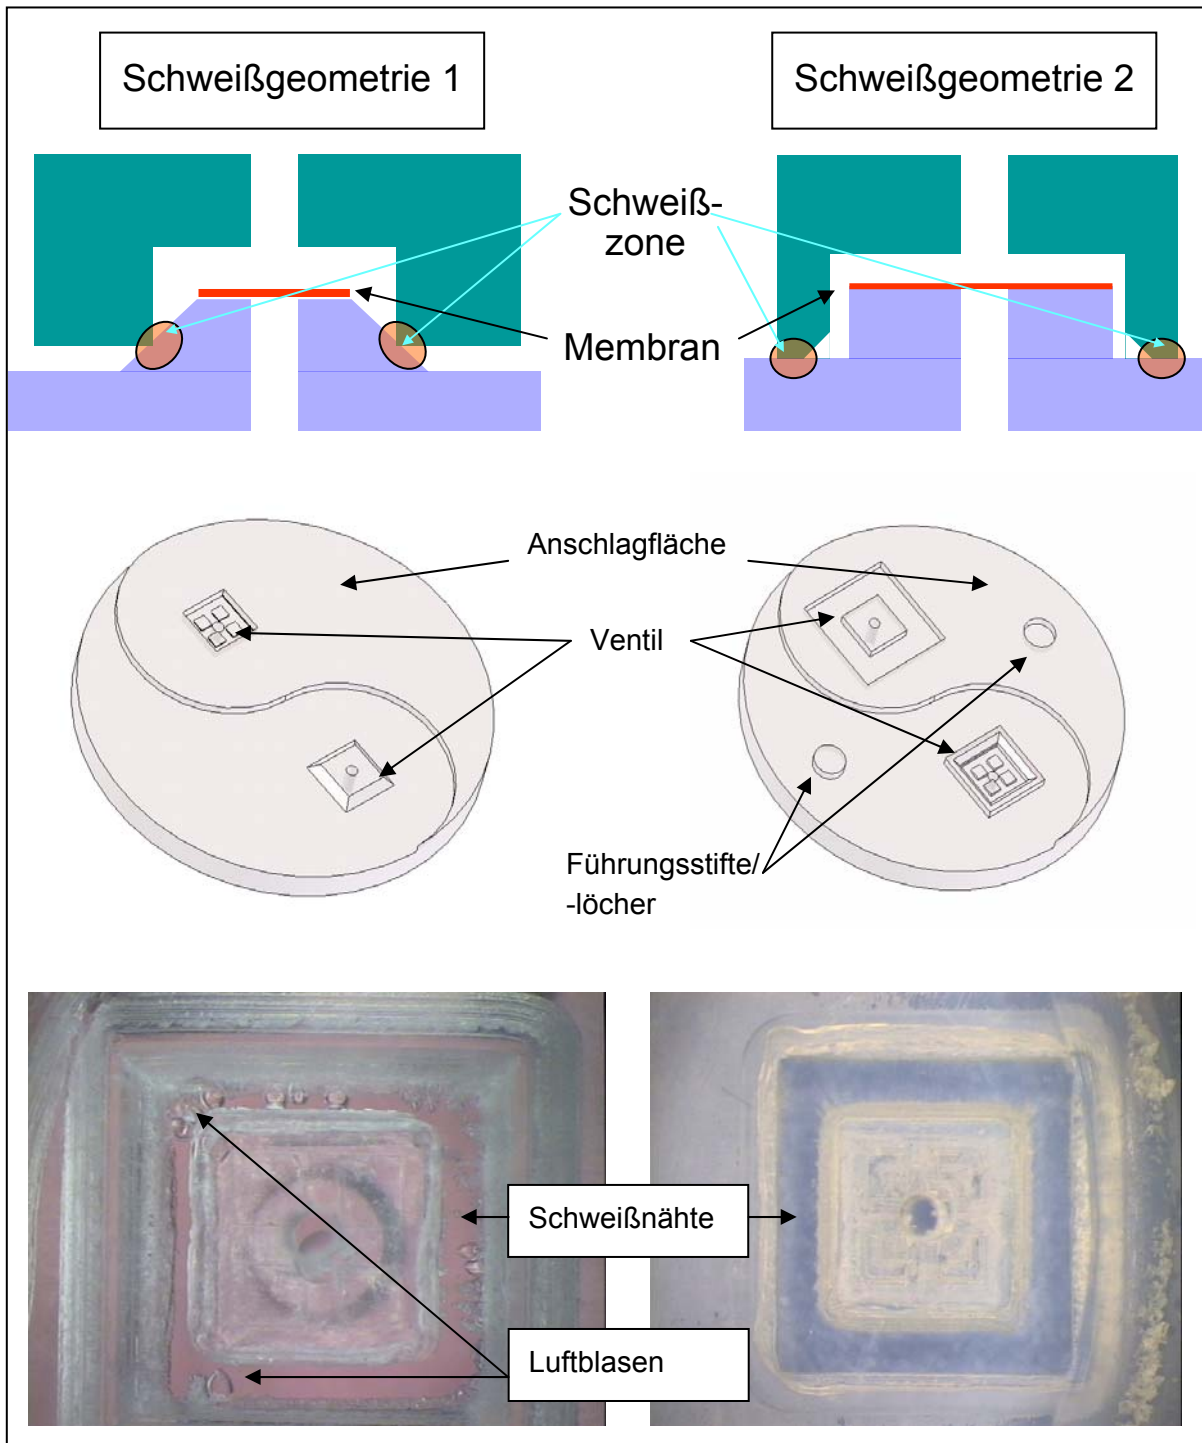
Konstruktion der Schweißgeometrie und Ventilscheiben
